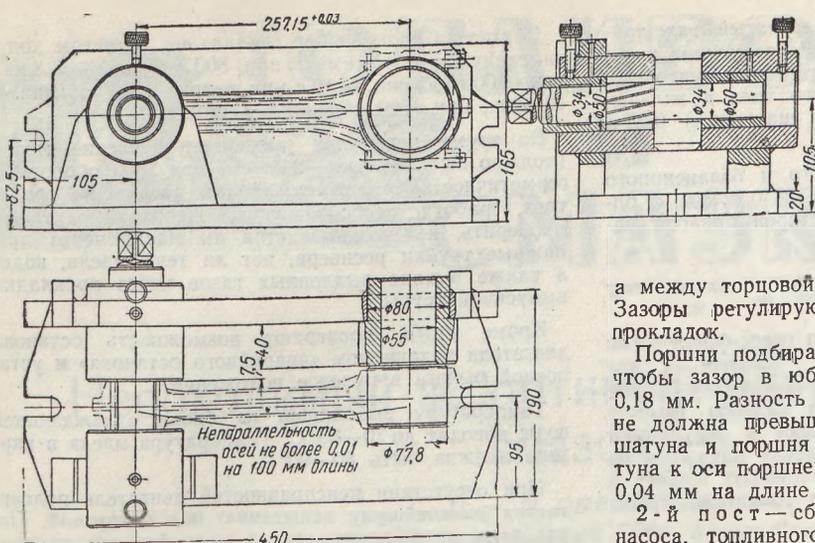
Приспособление для развертки втулки верхней головки шатуна.
